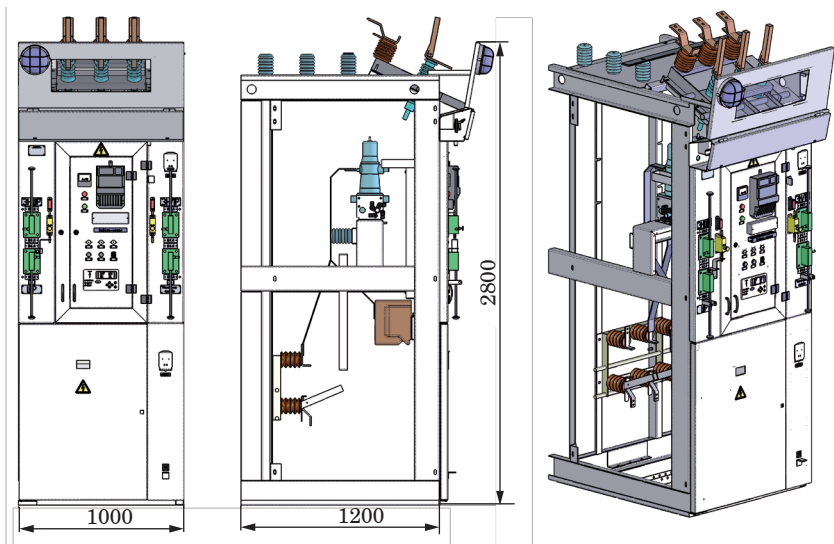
Габаритные и установочно-присоединительные размеры выключателя к ячейке КРУН (выкатное исполнение)
